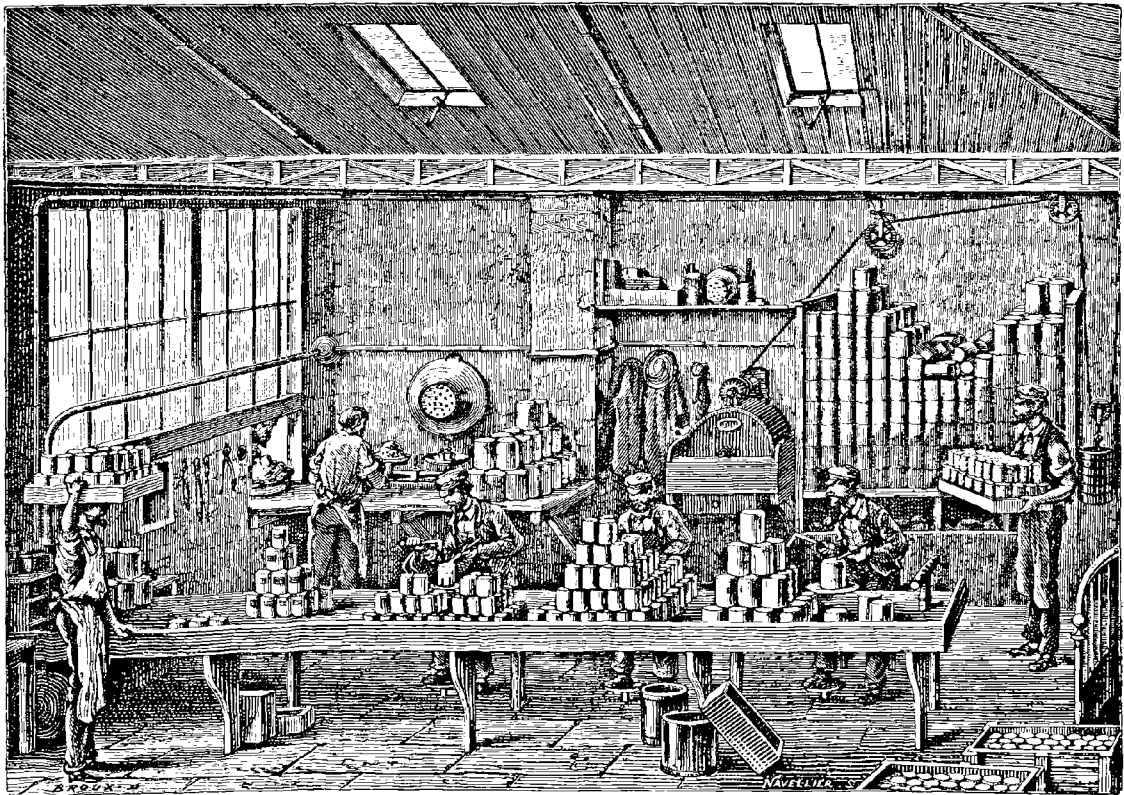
Atelier de remplissage et de soudure des boîtes.
